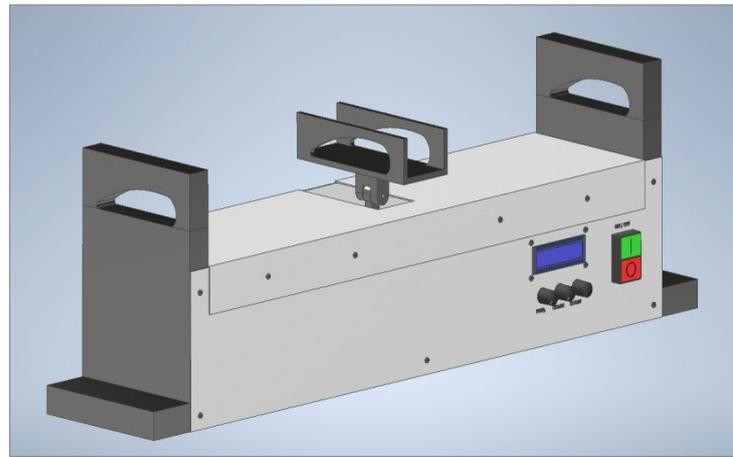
Tampa traseira com seus ajustes e pintura epóxi branca para fechamento traseiro da máquina.
